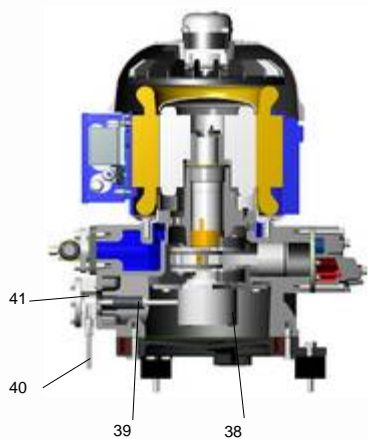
Schnittzeichnung mit interner Ölpumpe PI Bauform
